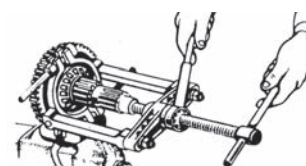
Спрессовка внутренней обоймы подшипника № 67512K1 с вторичного вала.
